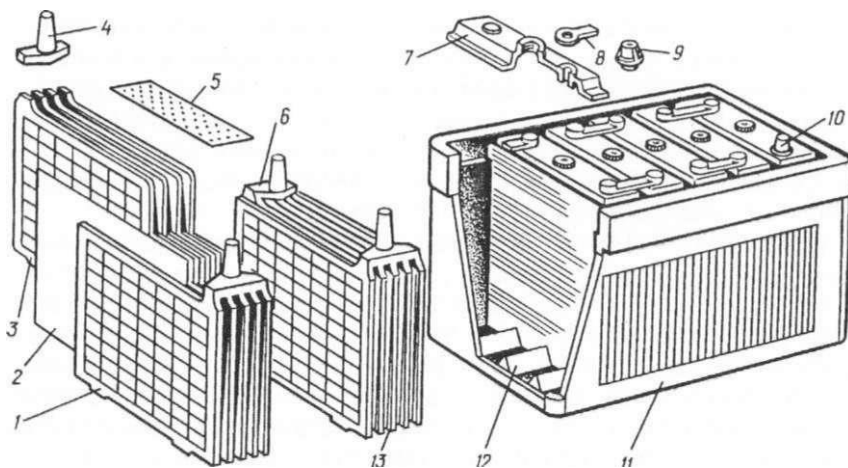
Стартерна акумуляторна батарея: 1 - негативна пластина; 2 - сепаратор; 3 - позитивна пластина; 4 - борн; 5 - сітка; 6 - місток; 7 - кришка; 8 - перемичка; 9 - пробка; 10- клемма; 11 - моноблок; 12 - призма; 13 - блок електродів.
